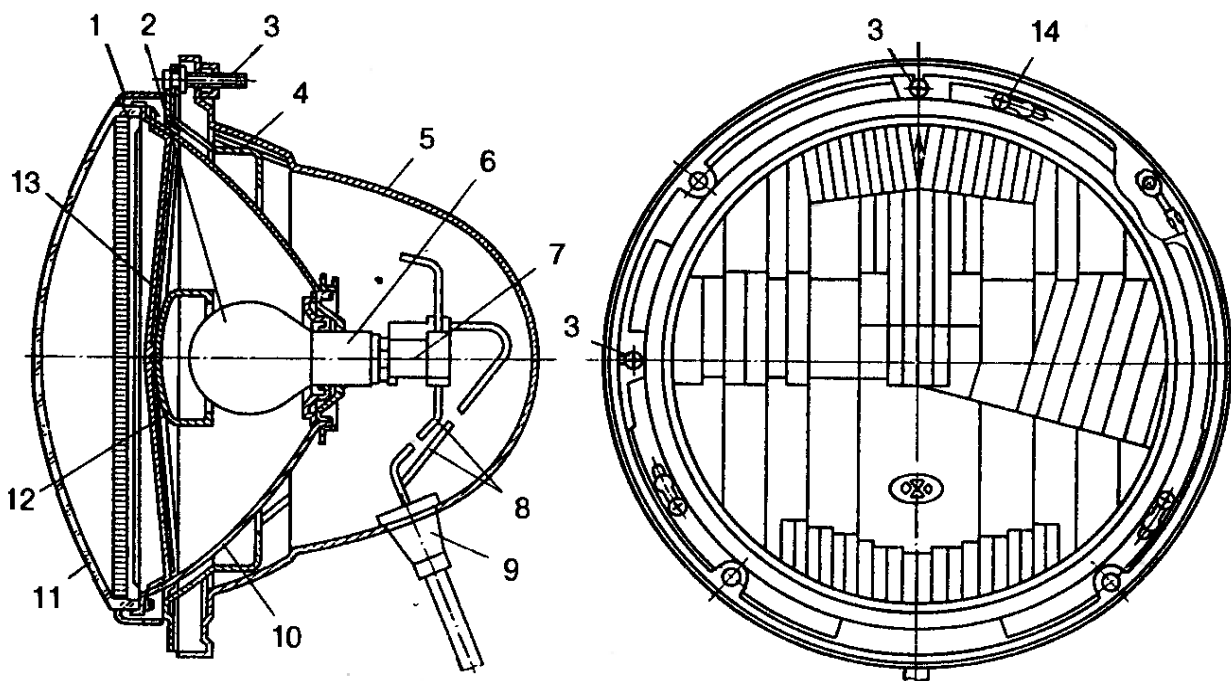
Автомобильная фара ФГ140 [1]: 1 - внутренний ободок; 2 - лампа; 3 - регулировочный винт; 4 - опорное кольцо; 5 - корпус; 6 - цоколь лампы; 7 - соединительная колодка; 8 - провода; 9 - держатель проводов; 10 - отражатель; 11 - рассеиватель; 12 - экран; 13 - держатель экрана; 14 - винт крепления ободка
